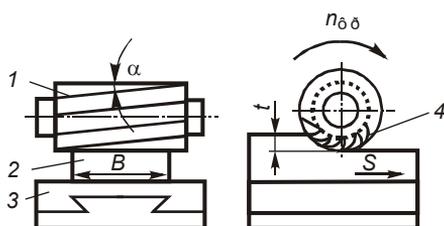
Схема фрезерования детали цилиндрической фрезой с винтовым зубом
